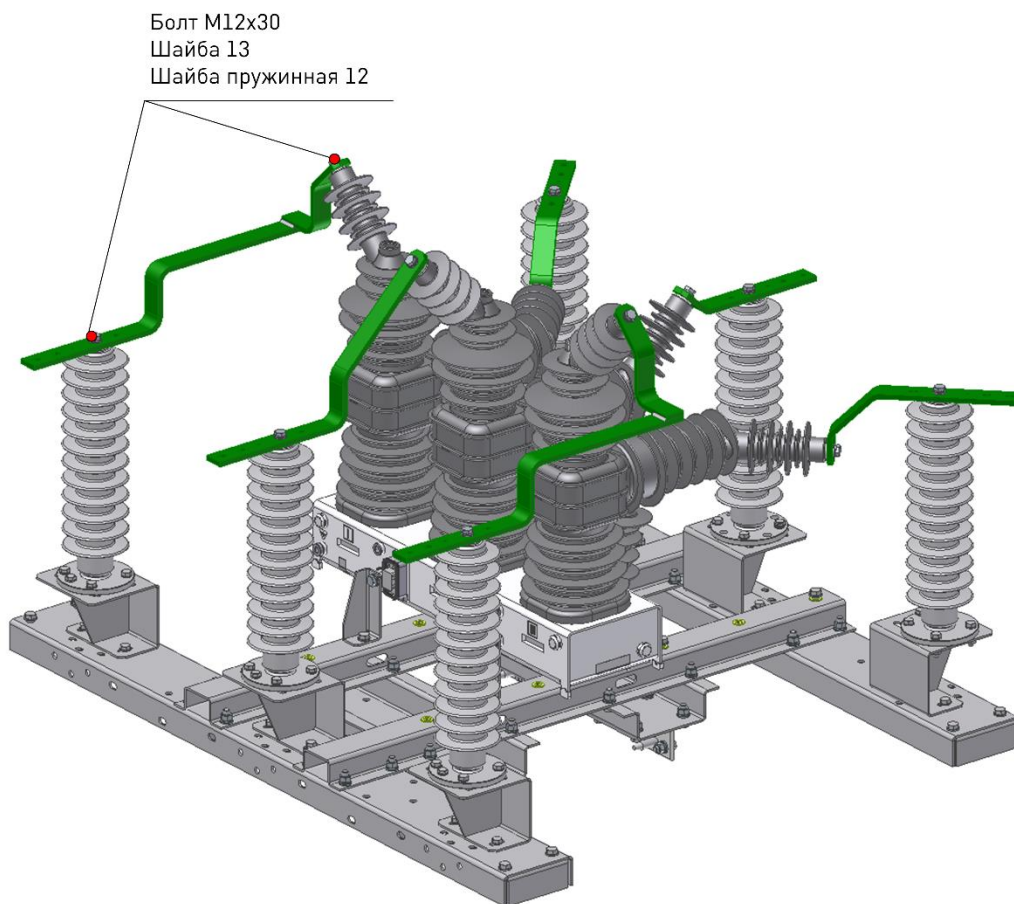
Сборка ошиновки с креплением к ОПН «ЗЭУ»
